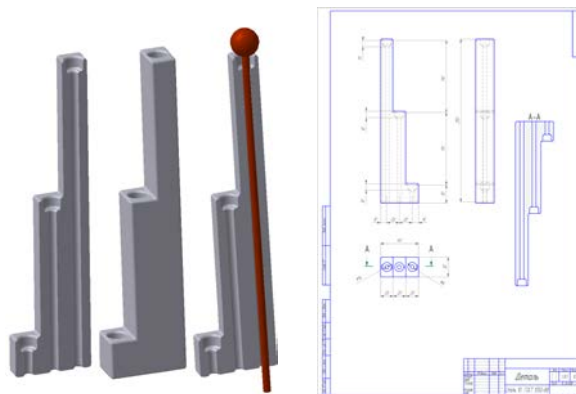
3D модель и рабочий чертеж блока датчиков
